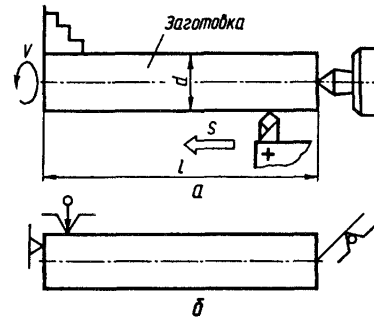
Закріплення довгої заготовки у патроні: а - з підтримуванням заднім центром;
